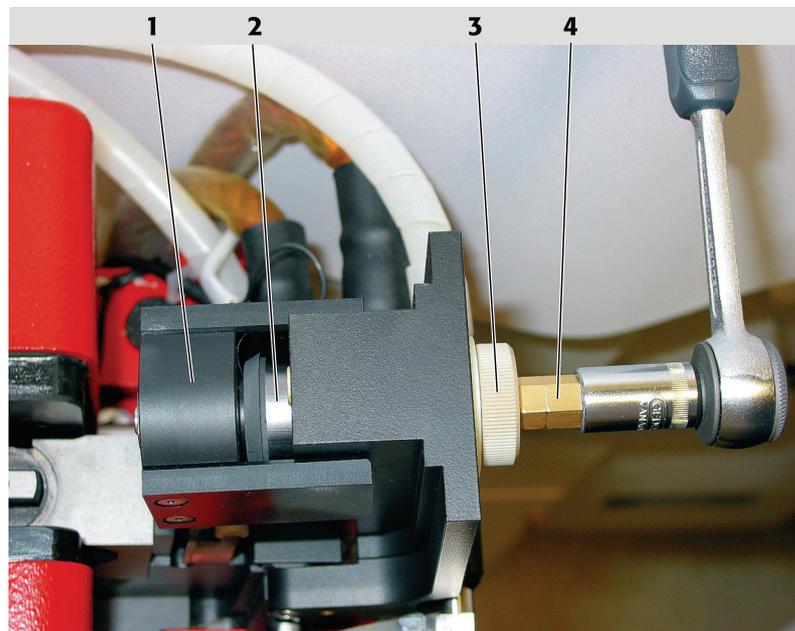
Elektrode mit Einziehwerkzeug an die Backe angesetzt
